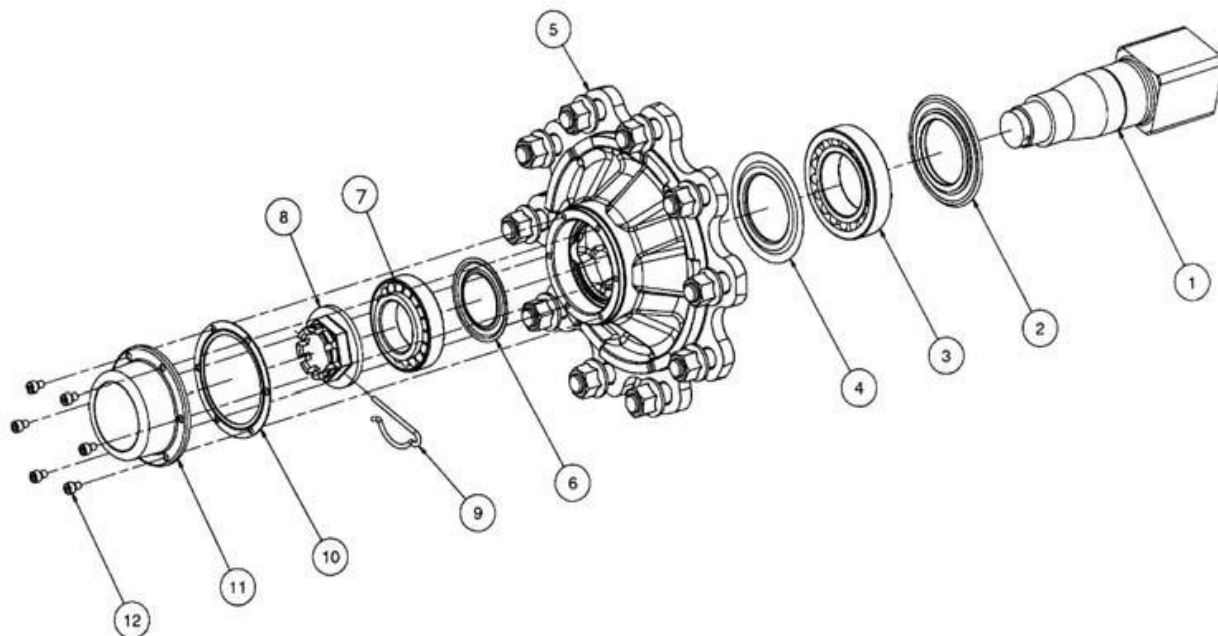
Схема регулировки подшипников ступиц колес ПР-9
